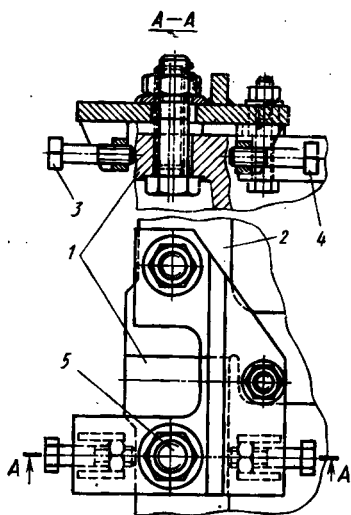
Приспособление для сборки вертикального стыка цилиндра среднего и низкого давления турбины К-300-240:
